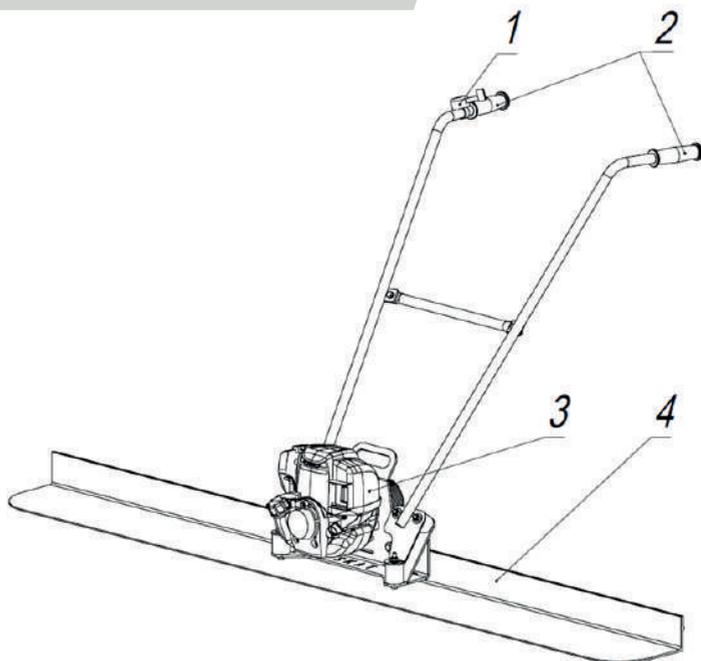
Схема устройства VPK SKAT Z: 1 – рычаг регулировки оборотов, 2 – рукоятки управления, 3 – двигатель, 4 – алюминиевый профиль*.
